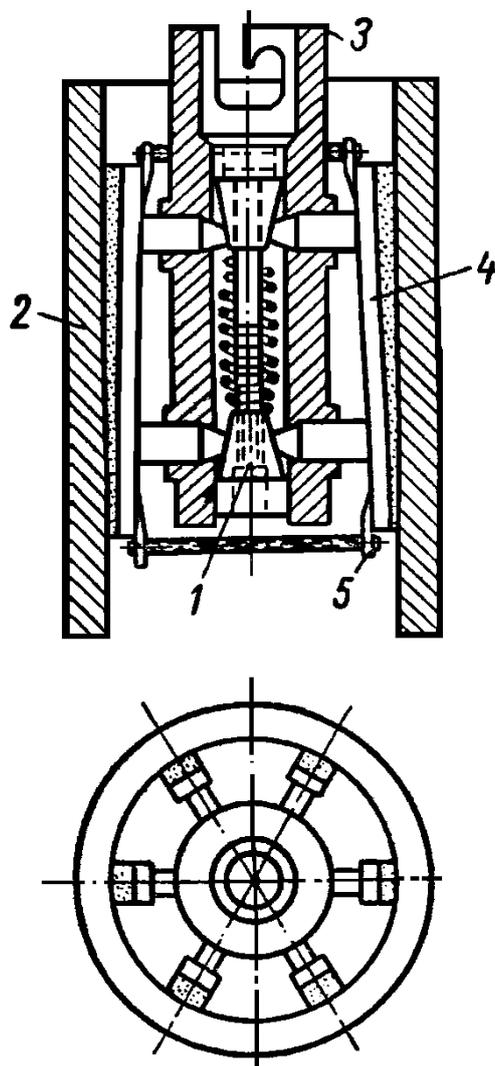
Схема конструкции хонинговальной головки: 1 – стержень; 2 – заготовки; 3 – шпиндель; 4 – абразивные бруски; 5 – цилиндр
